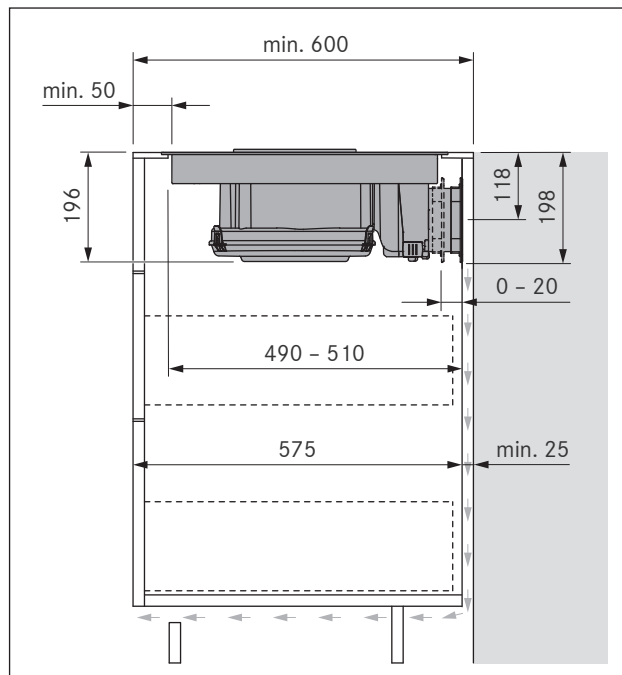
Dimensiones de montaje GP4U, profundidad de encimera 600 mm
